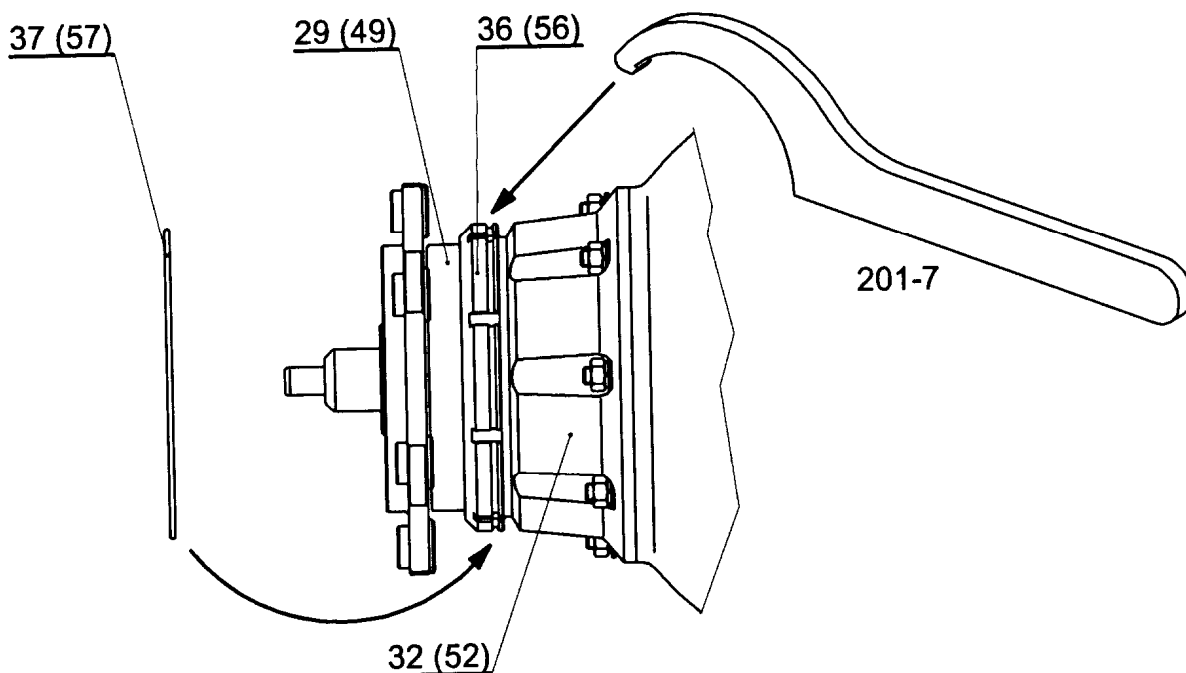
Nasazení rotoru rozvaděče P 7900.01
